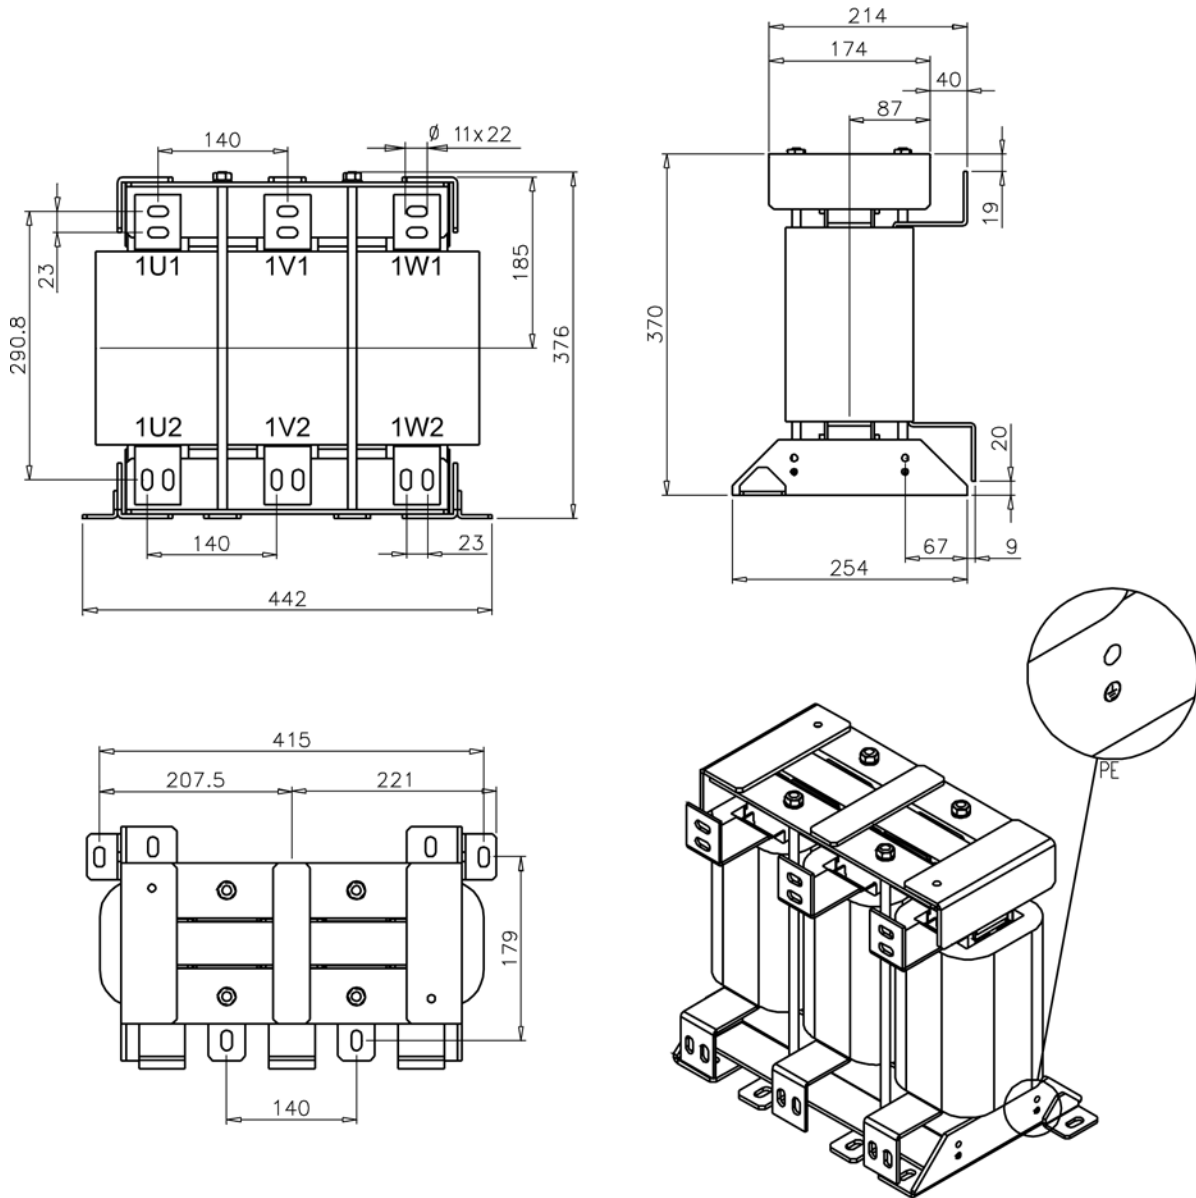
电源电抗器 6SL3000-0EE38-8AA0 的外形尺寸图，所有尺寸以 mm 为单位
